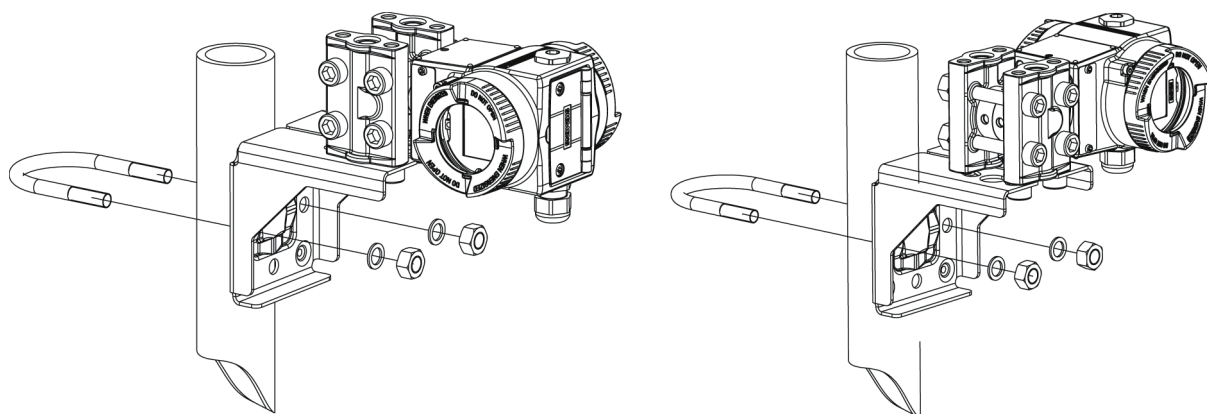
Befestigung des Messumformers mit Montagewinkel für senkrechte Wirkdruckleitungen
